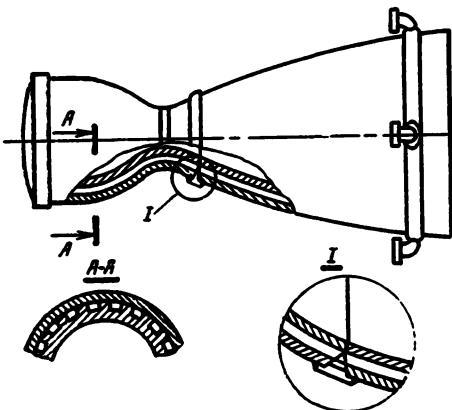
Сечение камеры сгорания с фрезерованными пазами
